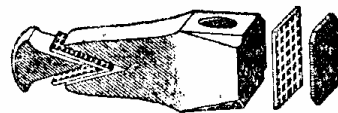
Pointe et talon rapportés par soudure.
